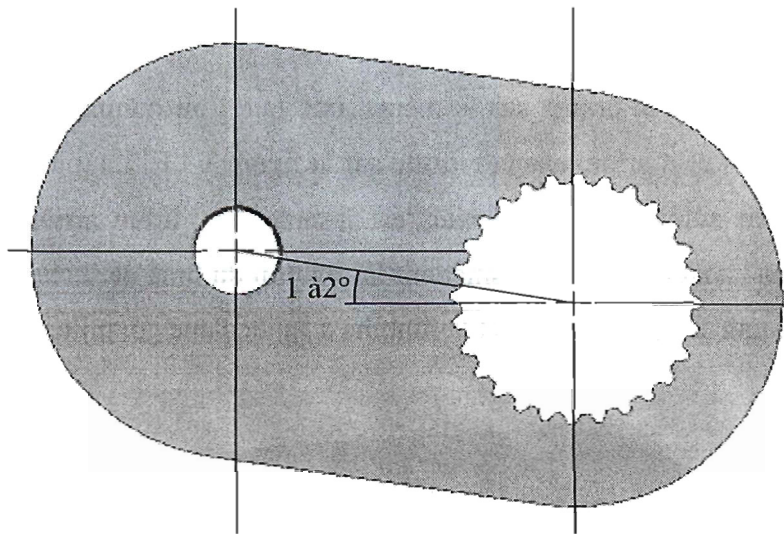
Angle d'installation du bras de levier au début de chaque essai
